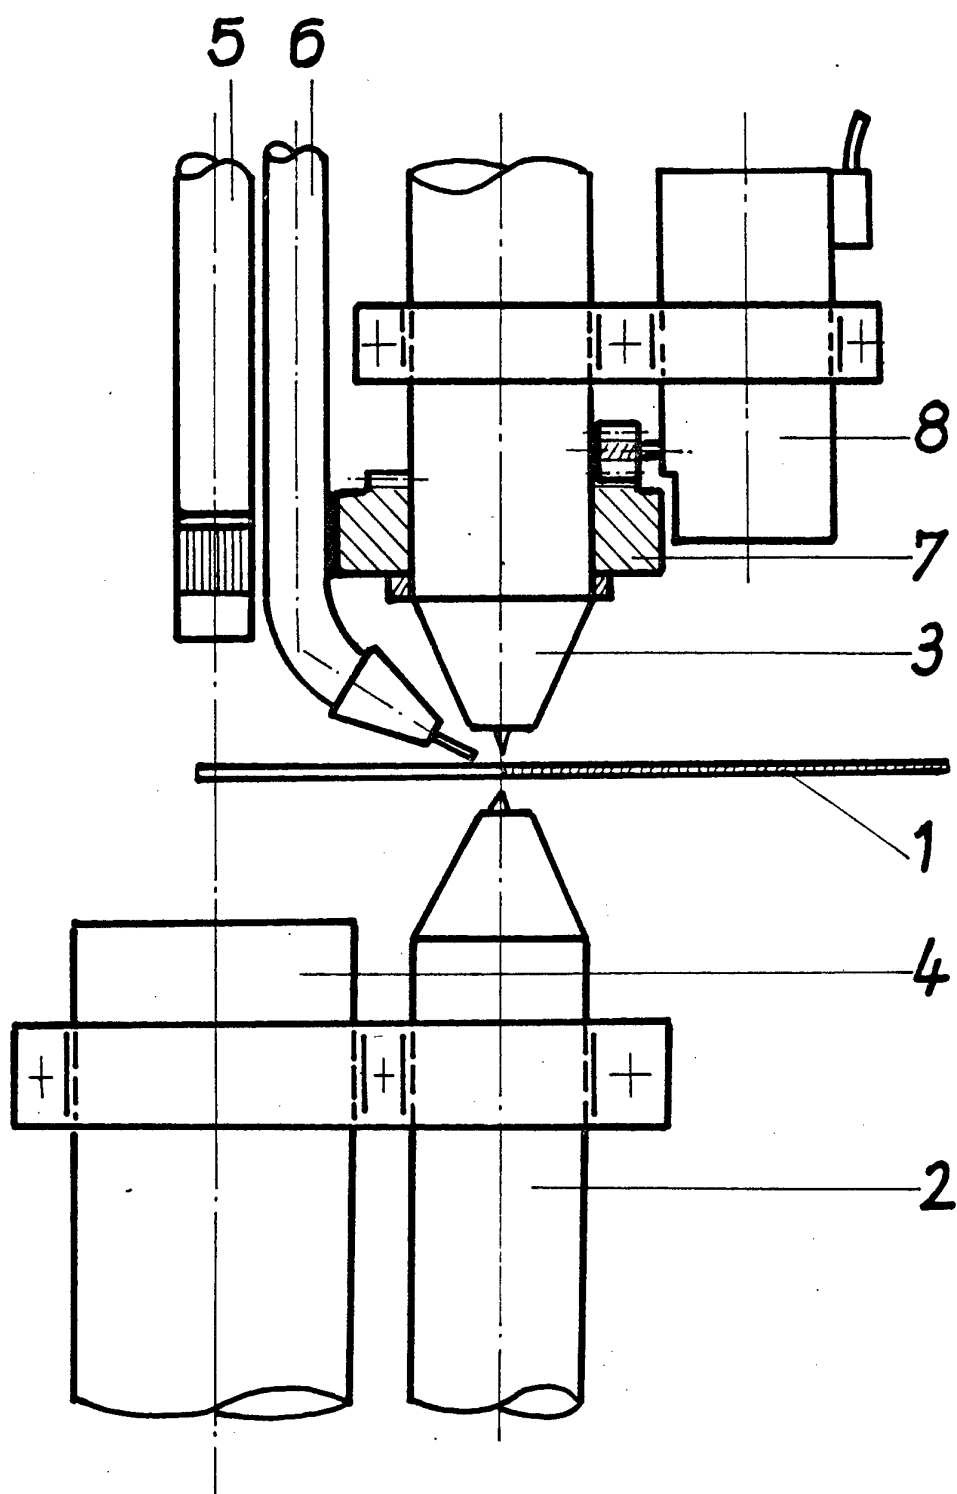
einen schematischen Querschnitt durch die Gerätetechnik während des Schweißprozesses
